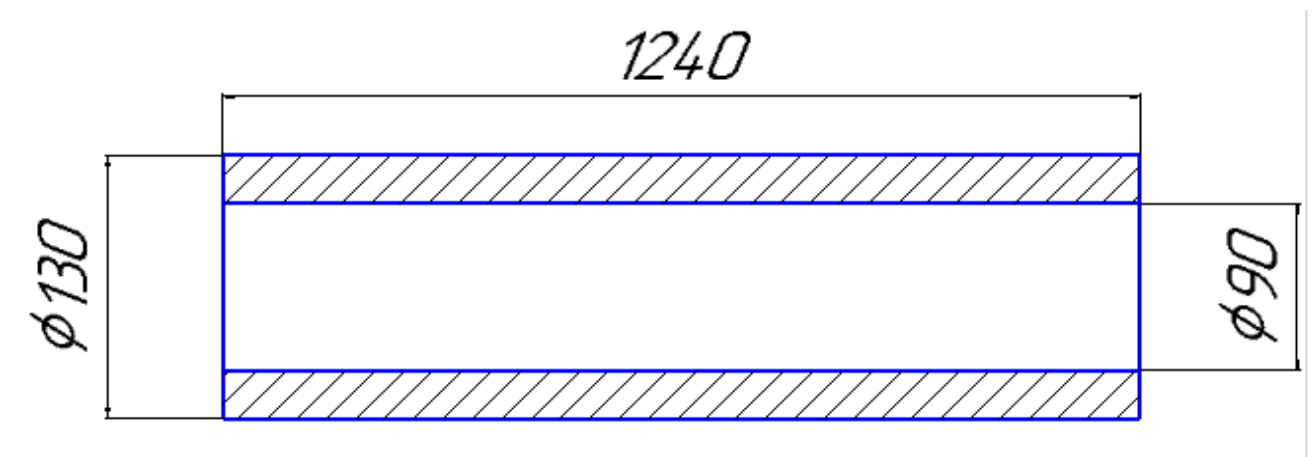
Виконане креслення заготовки корпуса ЧП-63
